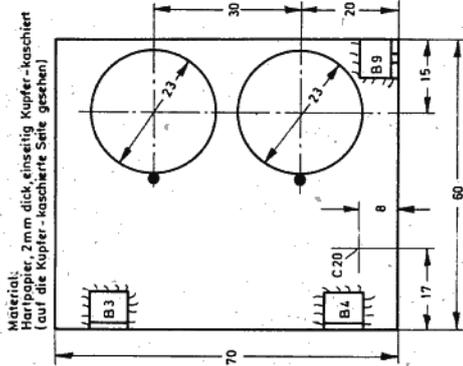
Montageplatte 1 mit aufgelöteten Befestigungswinkeln
